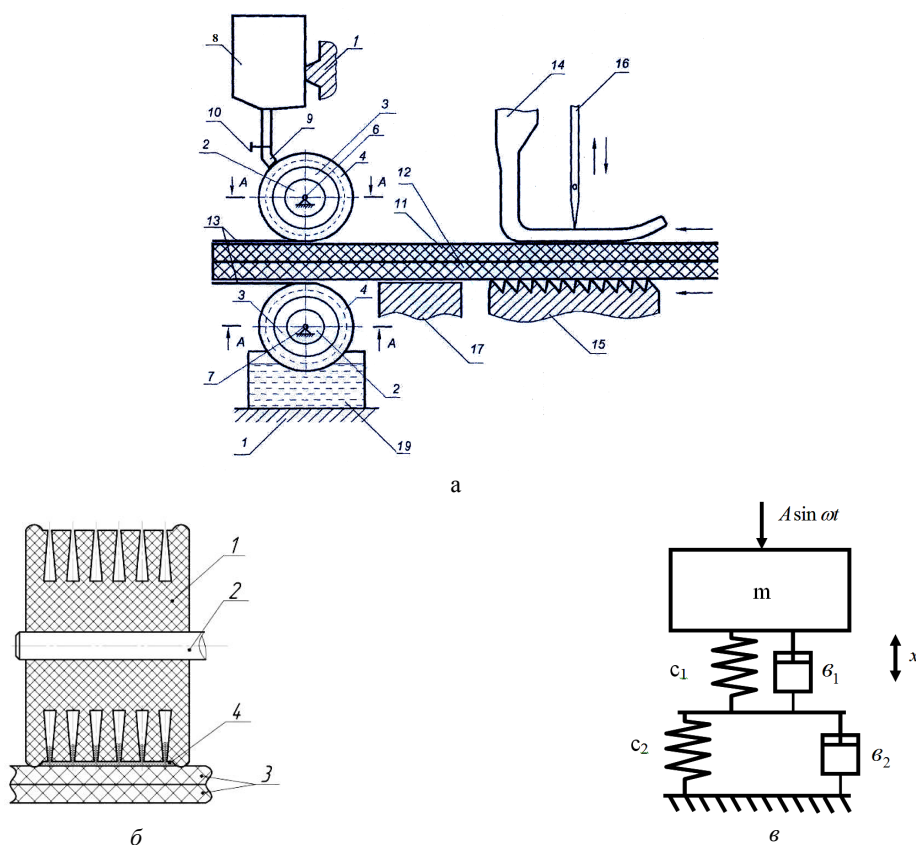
Устройства для нанесения полимерной композиции на стачиваемые детали края: а- общая схема; б – резиновый ролик; в – расчетная схема вертикальных колебаний оси ролика устройства
